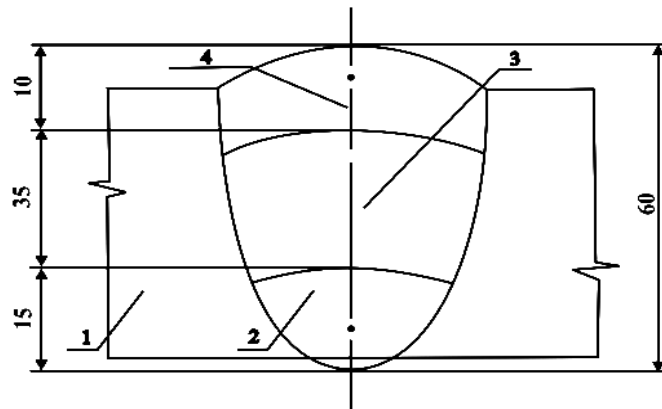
Схема зварного з'єднання, розбитого на ділянки: 1 – основний метал; 2 – коренева ділянка метал шва; 3 – середня ділянка; 4 – верхня ділянка
